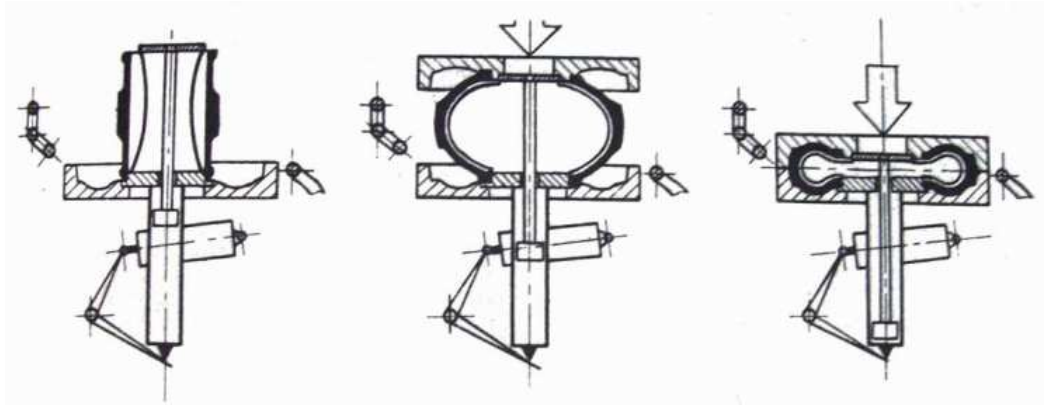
Vulkanizační lis Autoform se segmentovou formou [3]
